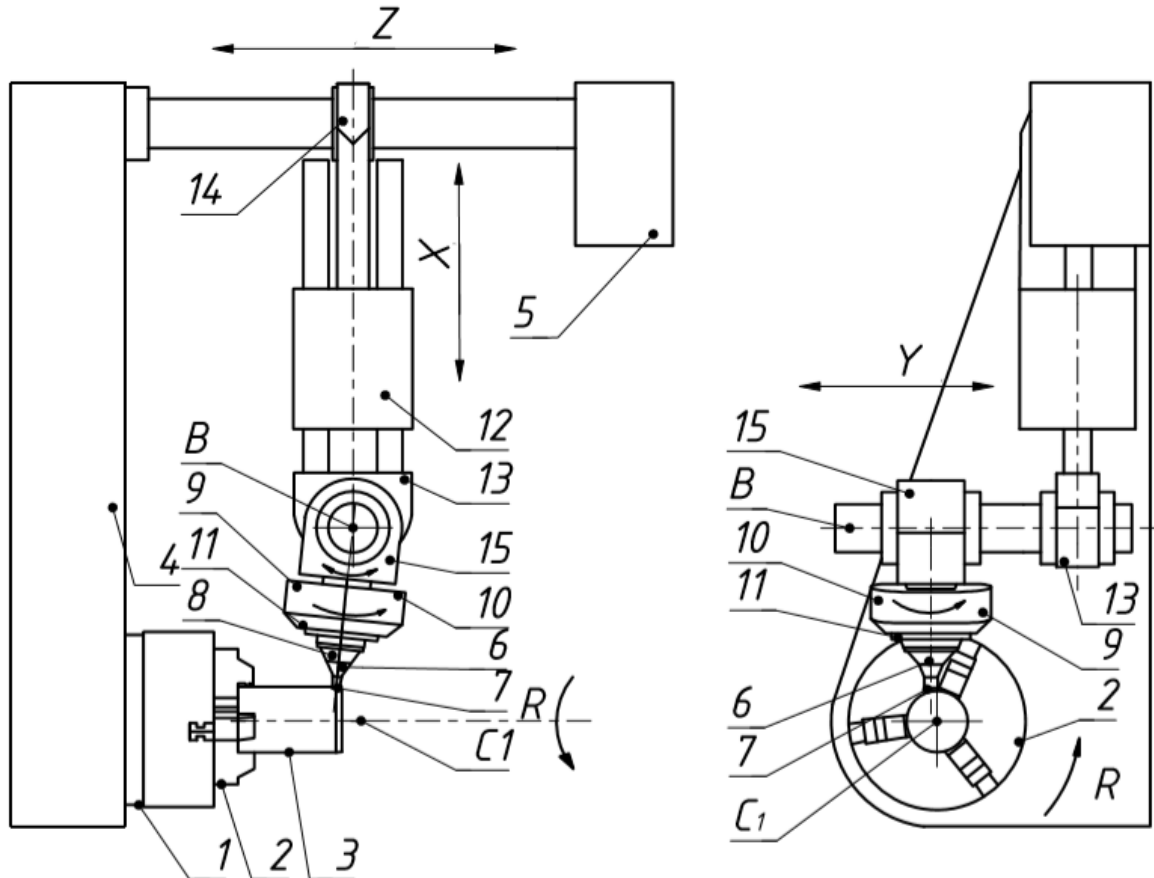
Верстат для ротаційного інструмента [10]
